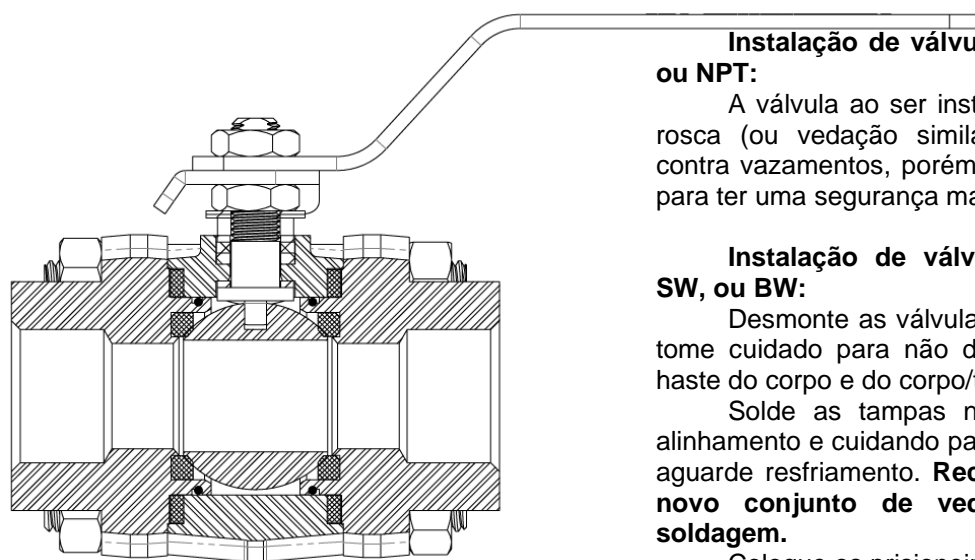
Corte transversal da VET Cl. 800 Montada.
